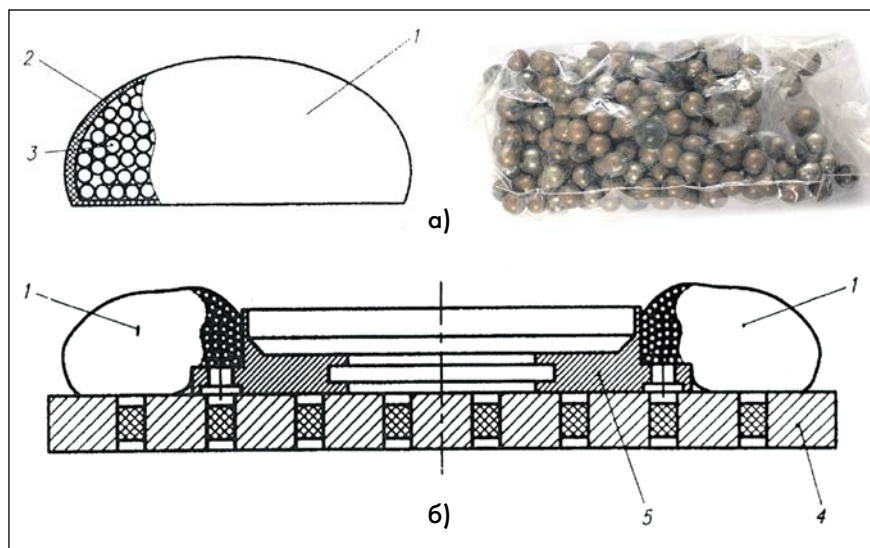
Гибкий прижим — а), зажатая прижимами деталь — б)
